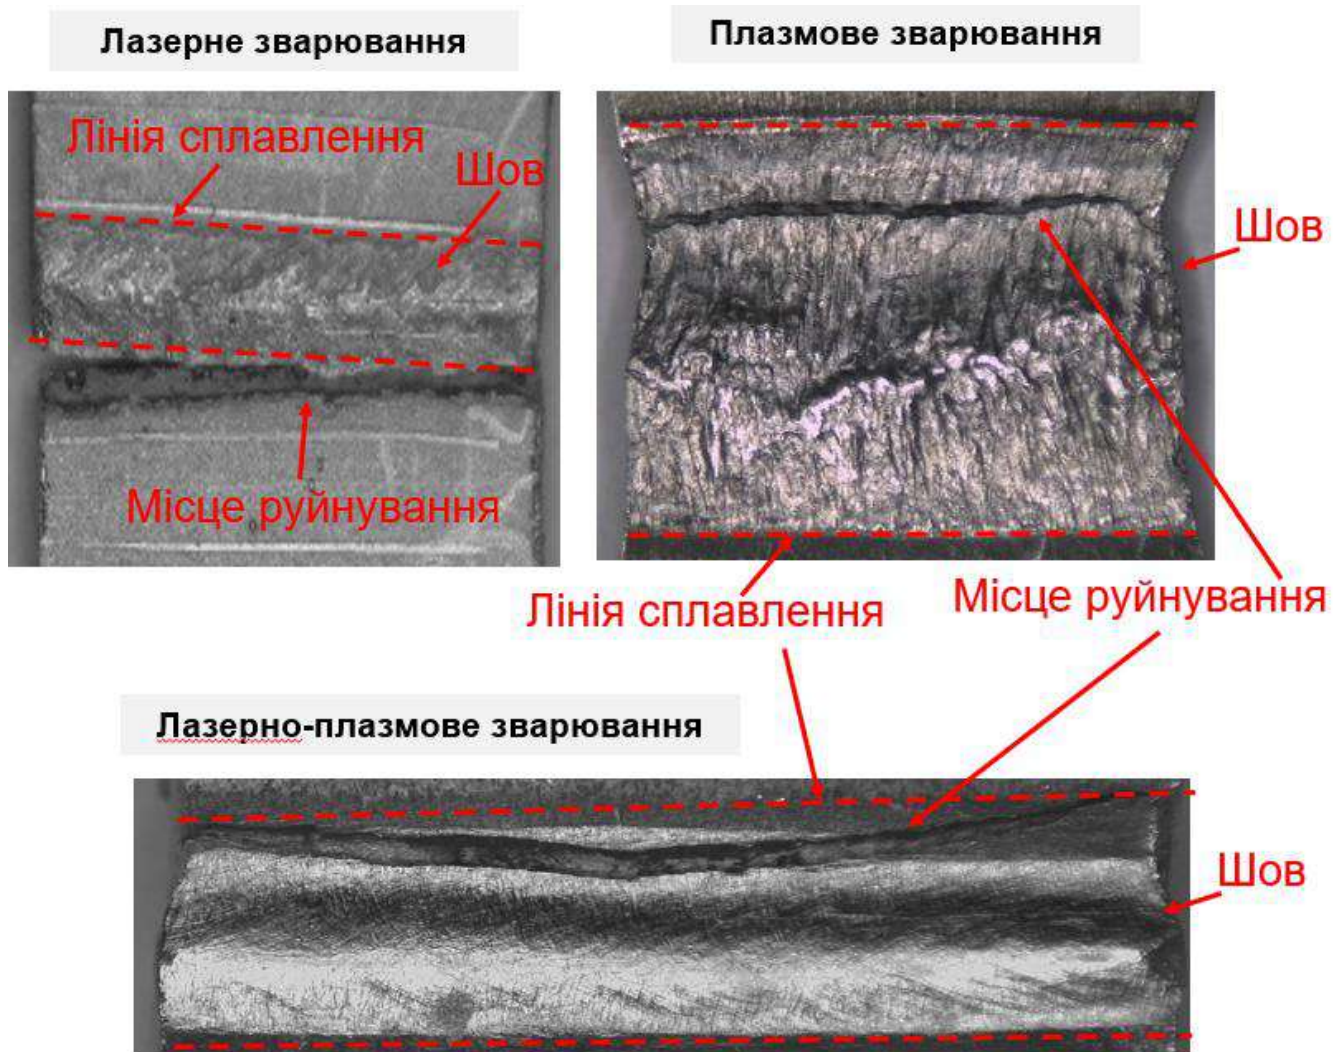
Фото місця руйнування, зразків зварних з'єднань зі сталі AISI 304.
